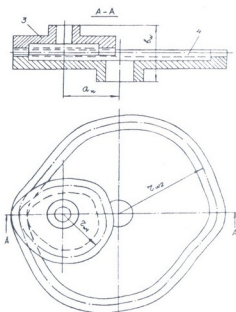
Торцевая зубчатая передача с некругло-круглыми колесами
